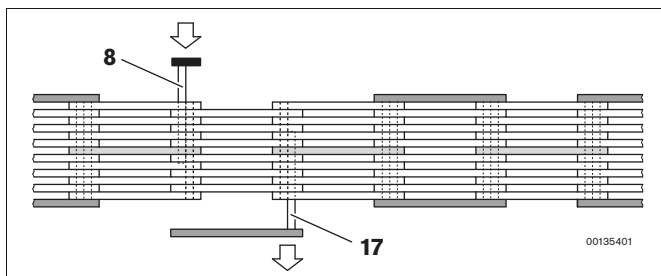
Insertar el pivote de cierre, retirar el muñón con la malla de soldado unida
